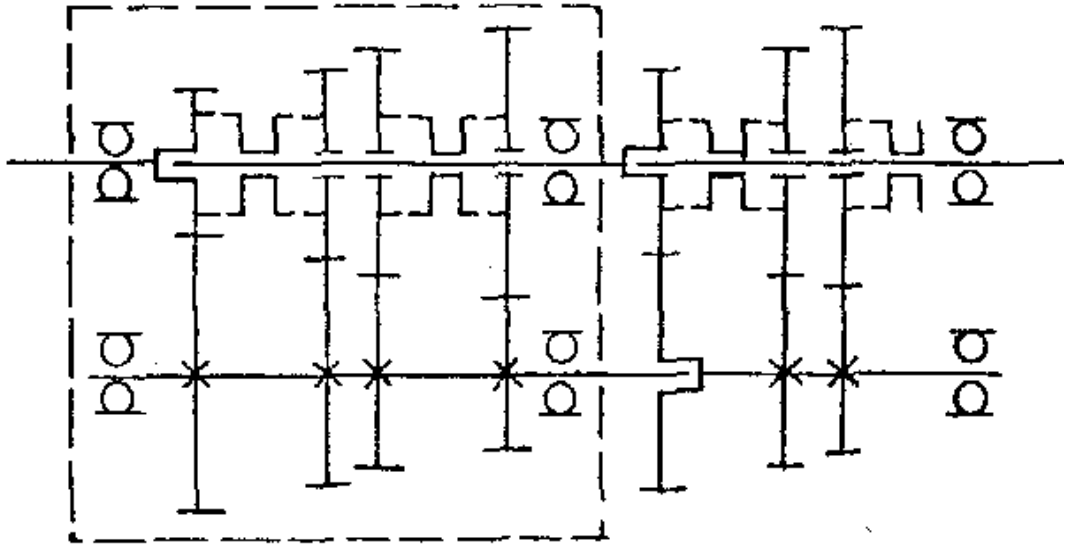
Кинематическая схема 4-х ступенчатой коробки передач в сборе с 3-х ступенчатым делителем
